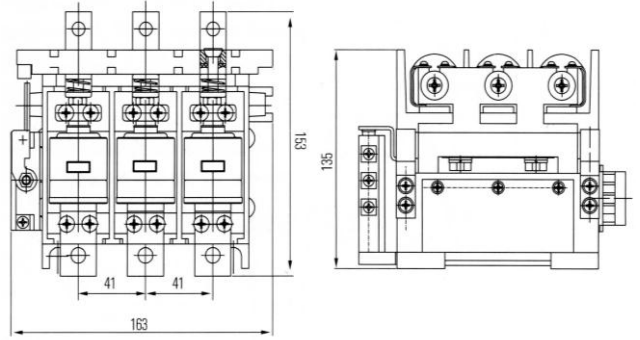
Габаритные размеры КВТ-1,14-80/125/160
